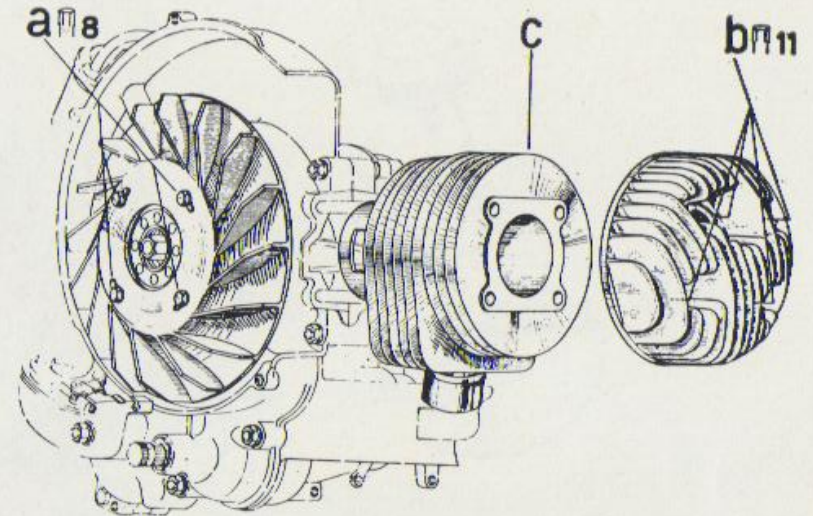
a) Turbine de ventilation (redresser les bords des plaquettes frein).
